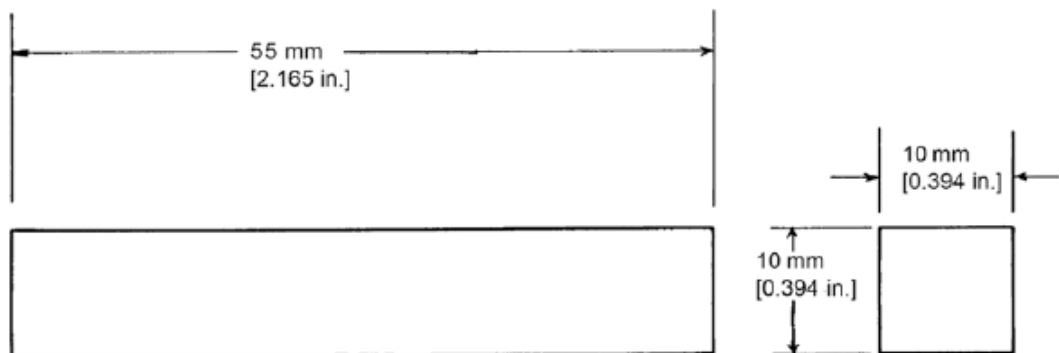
Dimensões para os corpos de prova de impacto [22].
